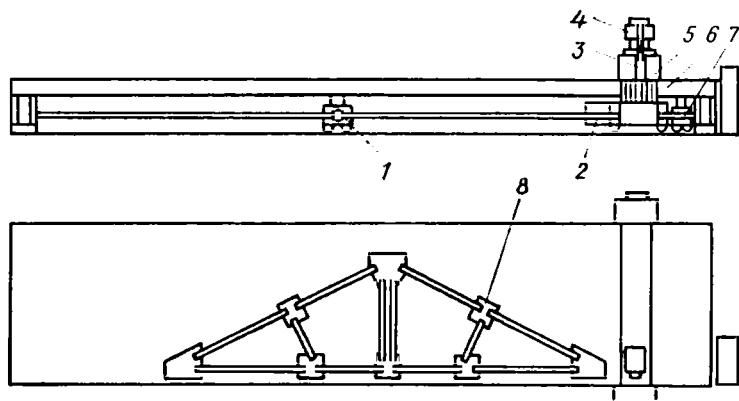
Схема агрегата сборки ферм и каркасов фронтонов ПДК210:
